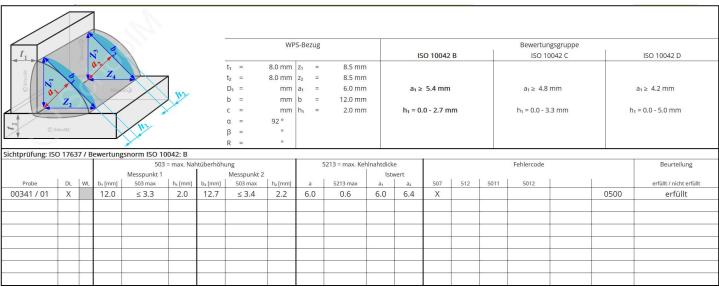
Schweißnaht Prüfprotokoll
